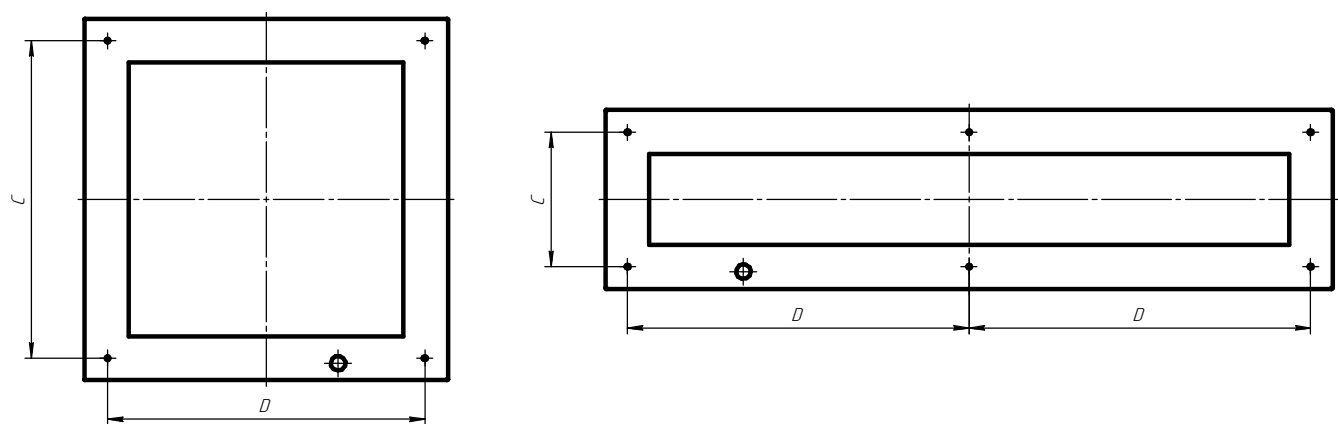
Размеры установочных отверстий скобы подвеса.
